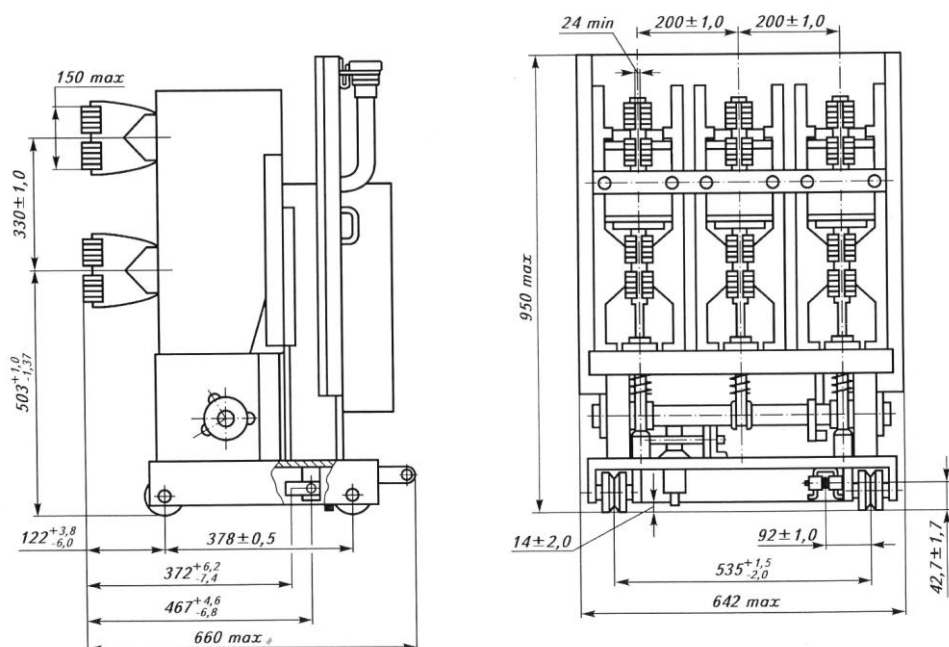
Внешний вид и габаритные размеры выключателя ВБЭК-10-40/3150У1
